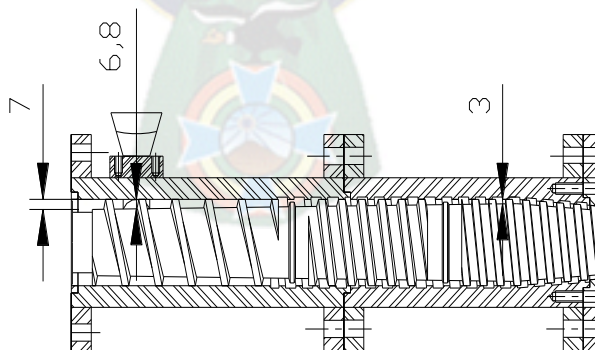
Sección del conjunto de tornillo y camisa de extrusión.
